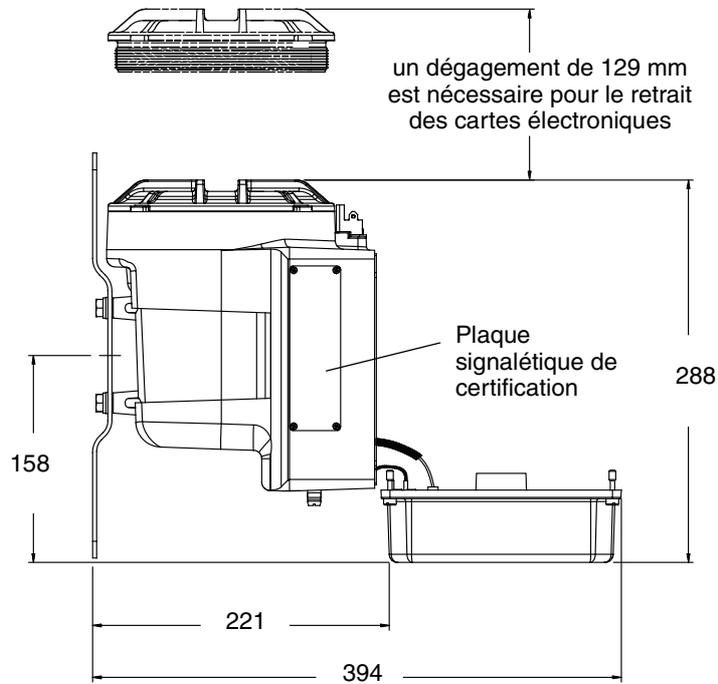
Dimensions du Modèle 3350 ou 3700 – vue de côté (entrées de câble)
